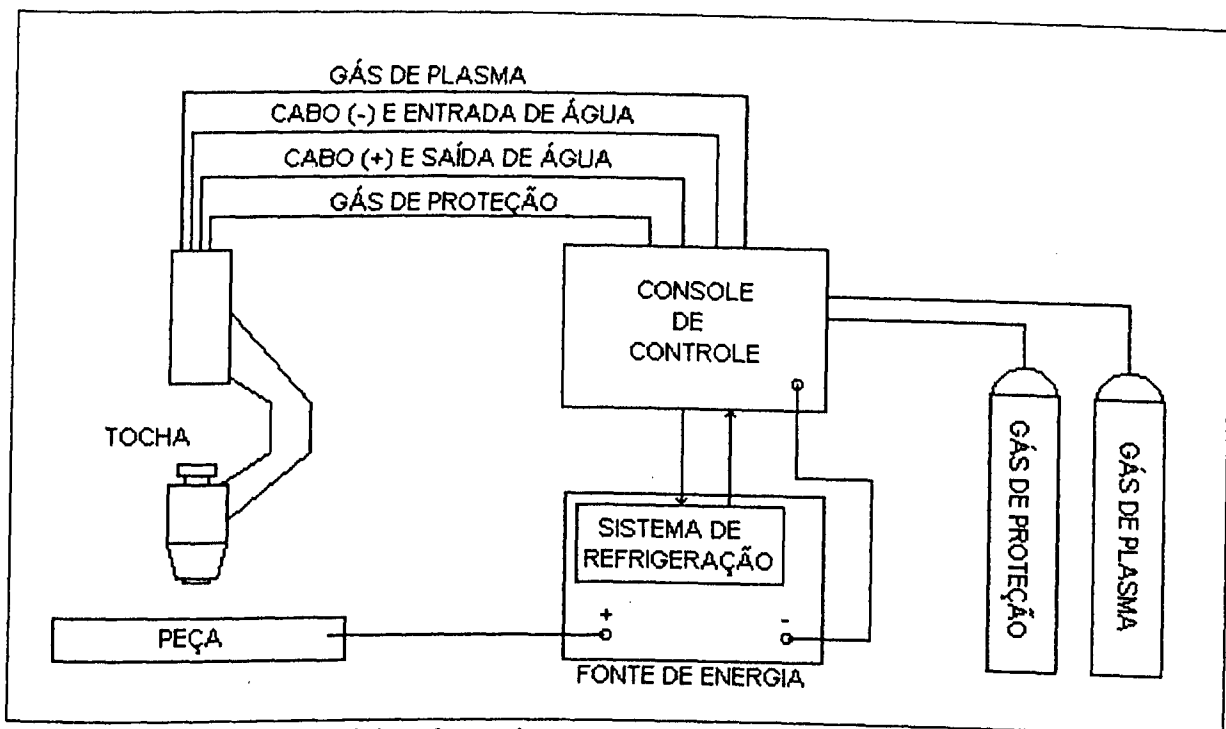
Conjunto básico de equipamentos utilizados na soldagem por plasma (AWS, 1991a).
